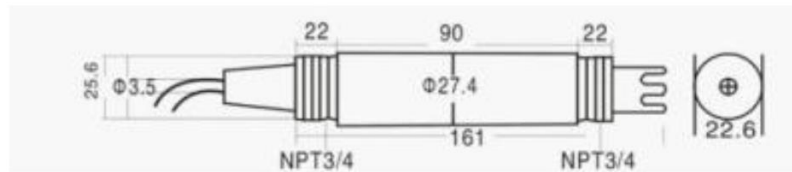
Dimensiones físicas de sensor de pH industrial.
